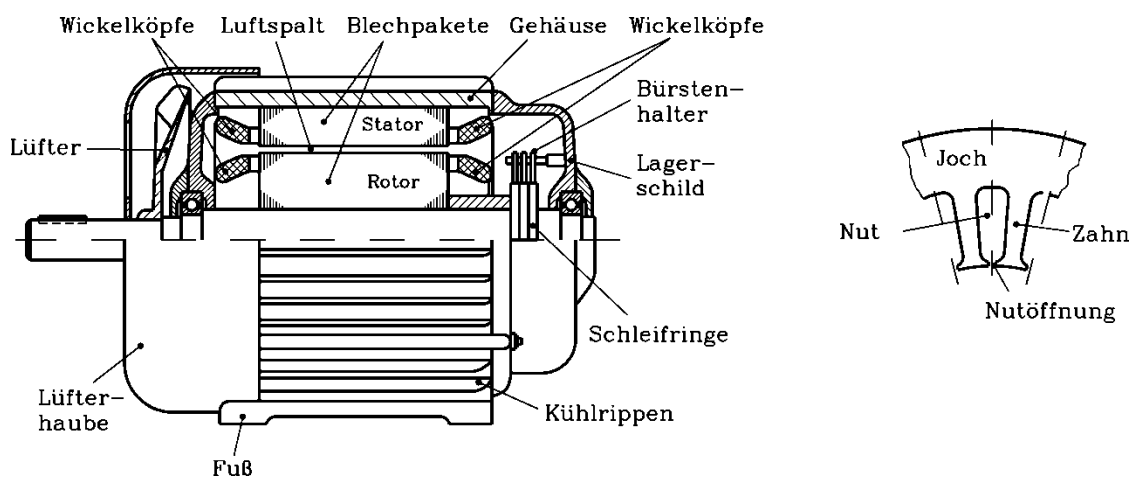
Längsschnitt durch einen oberflächengekühlten Schleifringläufer-Asynchronmotor und Detailansicht des Ständerblechschnitts mit einer Nut für die Wicklung
